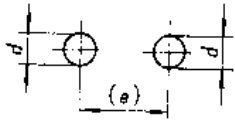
焊缝尺寸符号及数据标注原则
